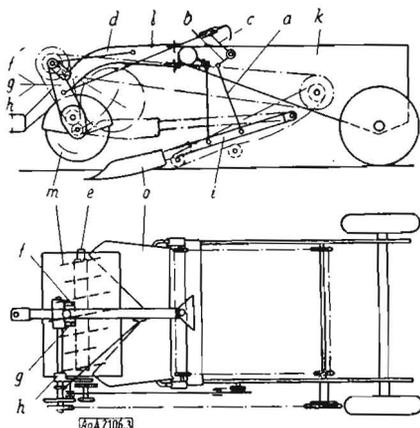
Krautentfernvorrichtung an Kartoffelerntemaschinen
